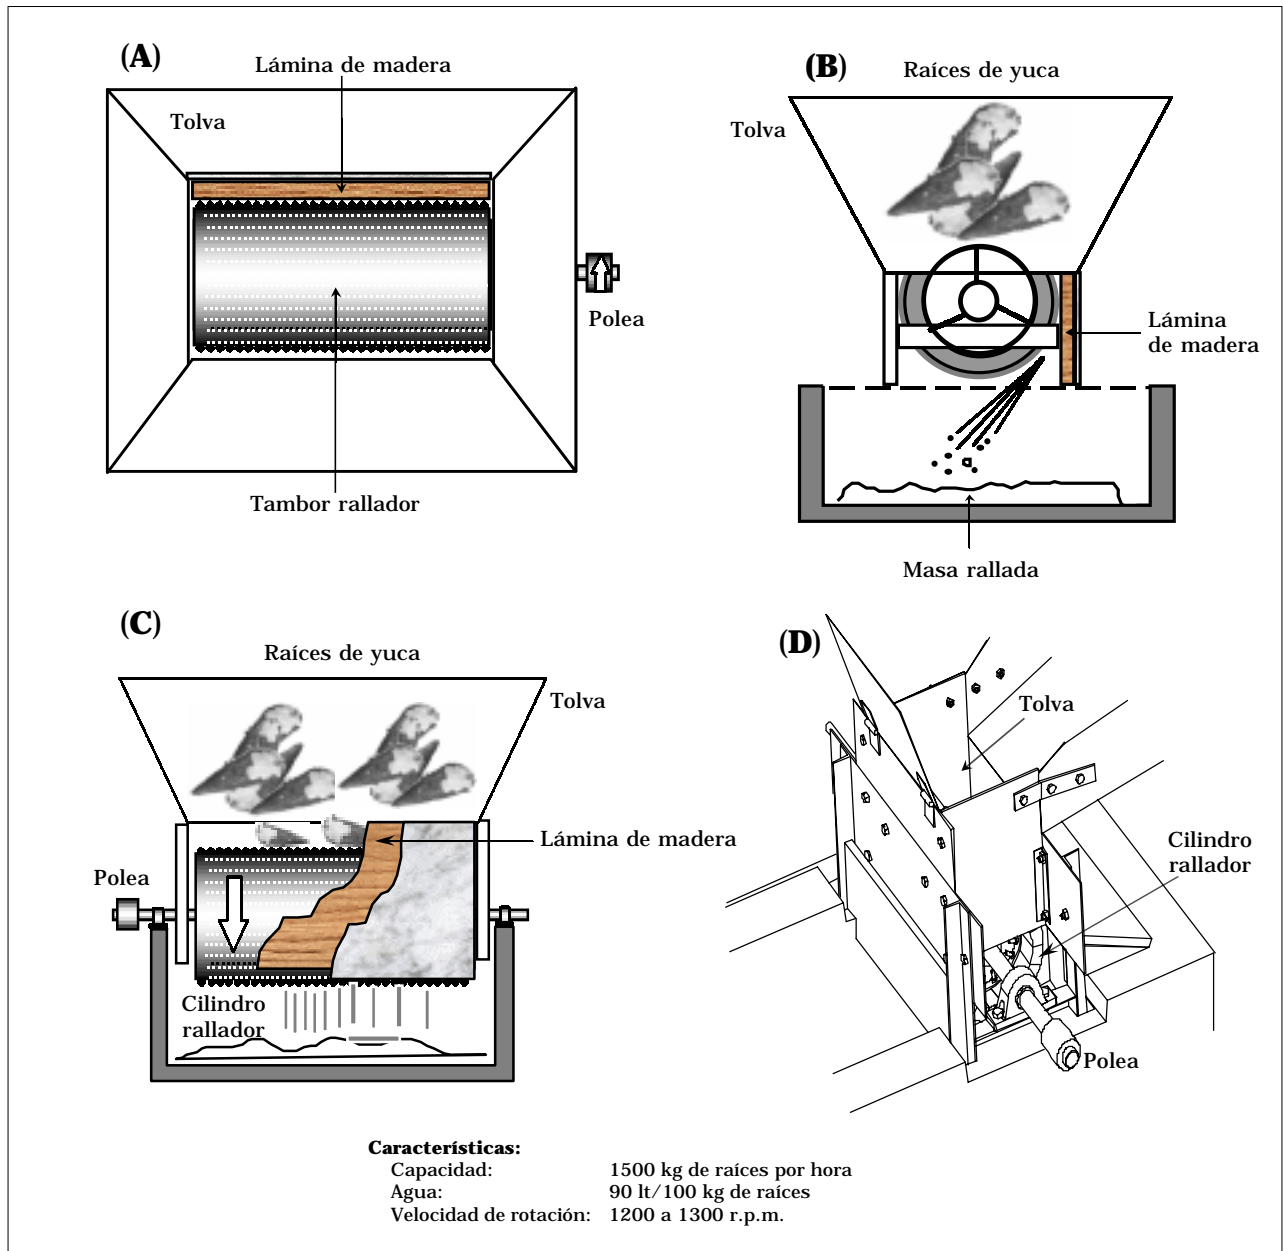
Rallador tradicional de raíces de yuca en que la superficie externa del cilindro es una lámina perforada. (A) Vista superior. (B) Vista lateral. (C) Vista frontal. (D) Dibujo técnico de una máquina ralladora.
